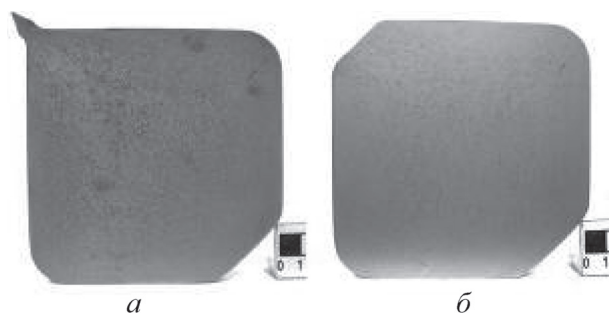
Внешний вид исходного сечения заготовки: а – с остатками перемычки; б – после удаления перемычки
